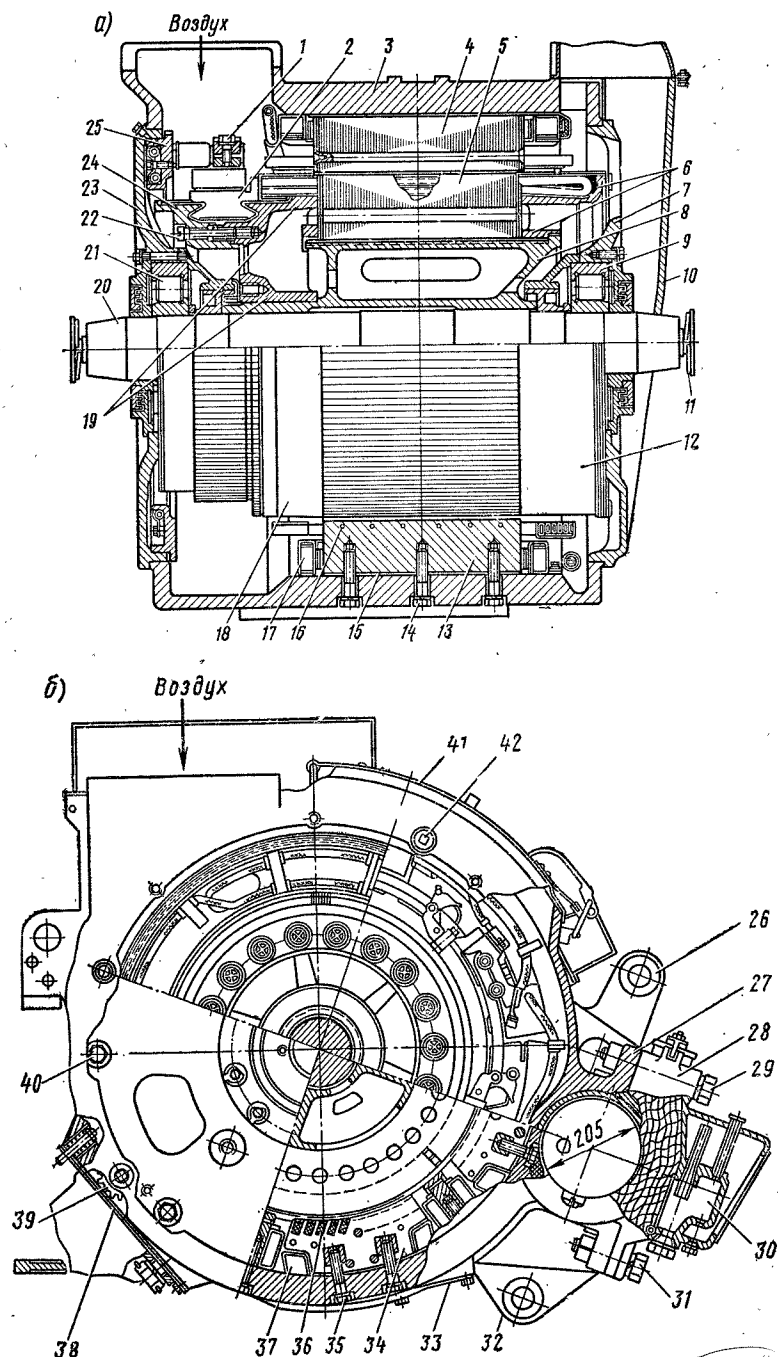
Продольный (а) и поперечный (б) разрезы тягового двигателя ТЛ-2К1
